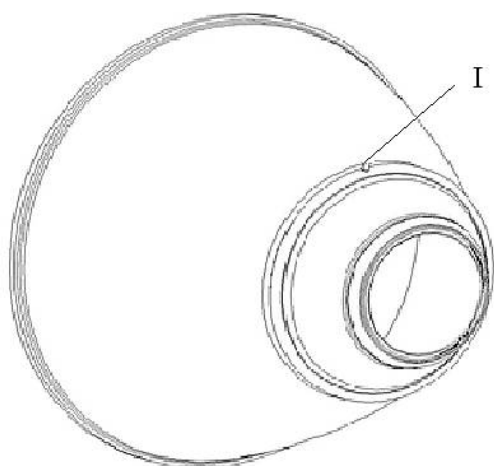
Общий вид двухслойной оболочки жидкостного ракетного двигателя
